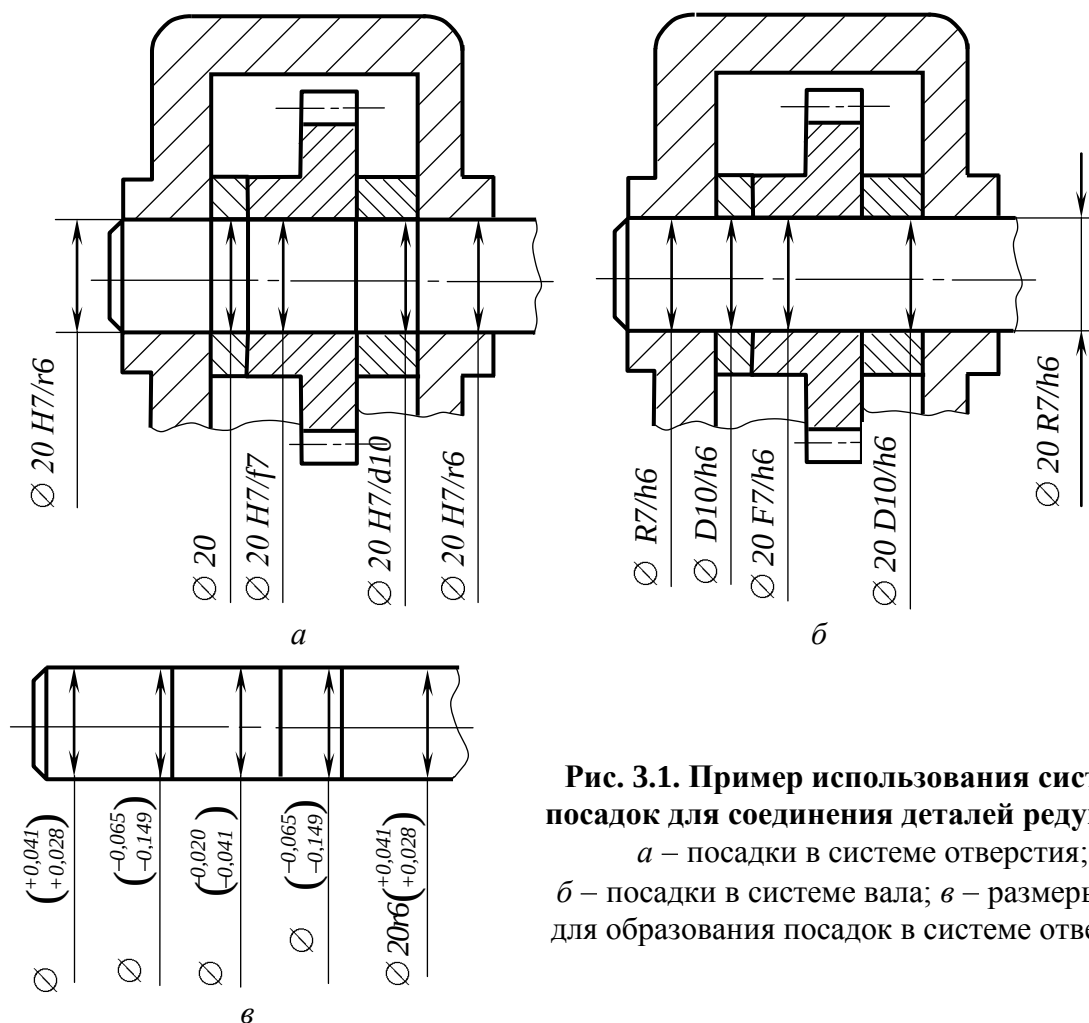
Пример использования системы посадок для соединения деталей редуктора:
